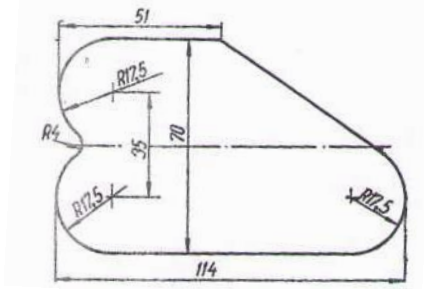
Заготовка стійки транспортеру ТВК-80А (деталь ТВК-4149)
